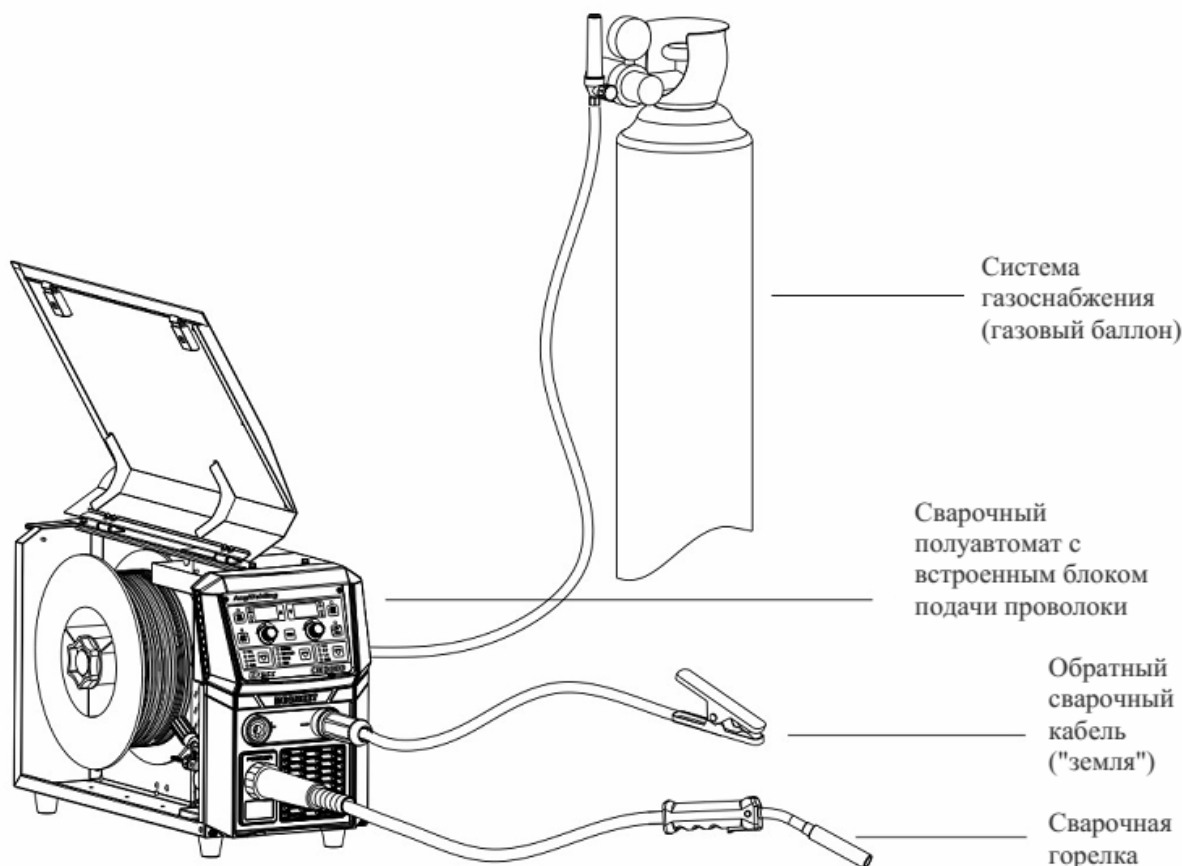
Состав оборудования сварочного полуавтомата
